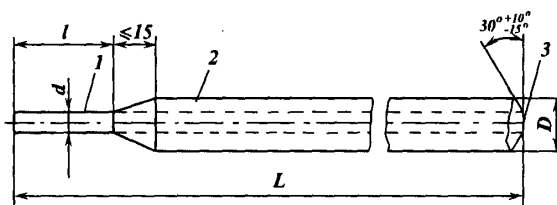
Покрытый сварочный электрод
